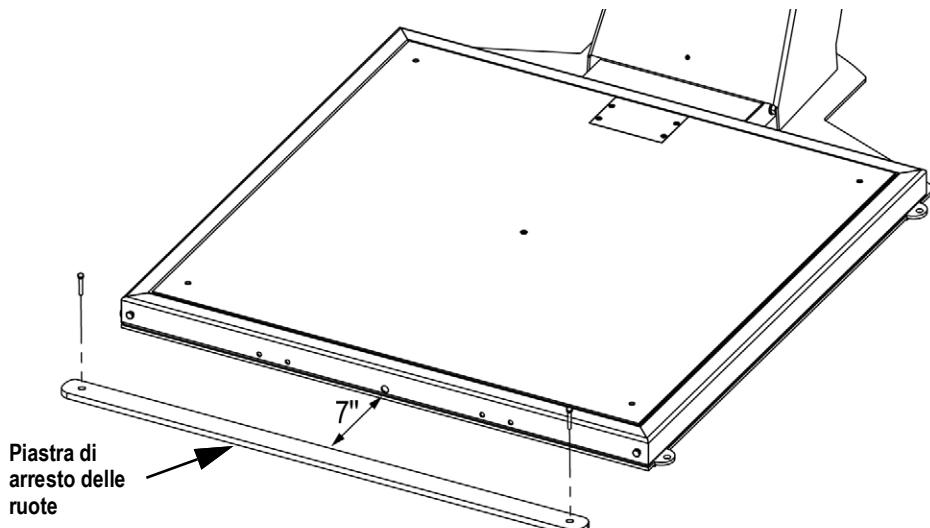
Piastra di arresto delle ruote del carrello elevatore
